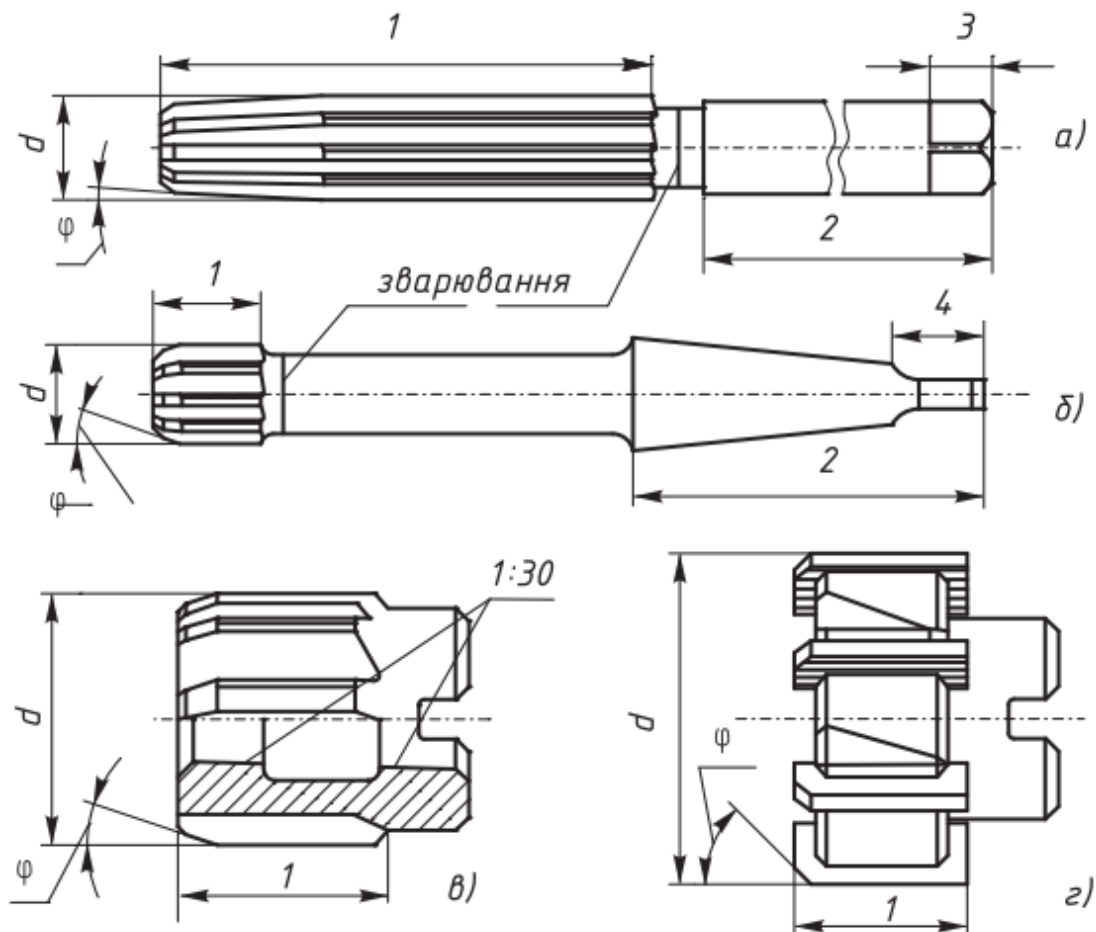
Типи розверток і їх геометричні параметри: а) суцільна ручна розвертка; б) – суцільна машинна розвертка; в) – суцільна насадна розвертка; г) – збірна насадна розвертка; 1 – робоча частина; 2 – хвостовик; 3 – квадрат для ручного кріплення; 4 – конус Морзе і лапка машинної розвертки; φ – кут заборного конусу; d – діаметр розвертки..
